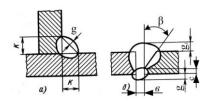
Обозначение конструктивных элементов сварных швов ( $\kappa$  – катет шва; g – усиление шва;  $\beta$  – угол разделки кромок; c – притупление;  $\epsilon$  - технологический зазор): а) тавровое соединение;  $\epsilon$ 0 стыковое соединение
